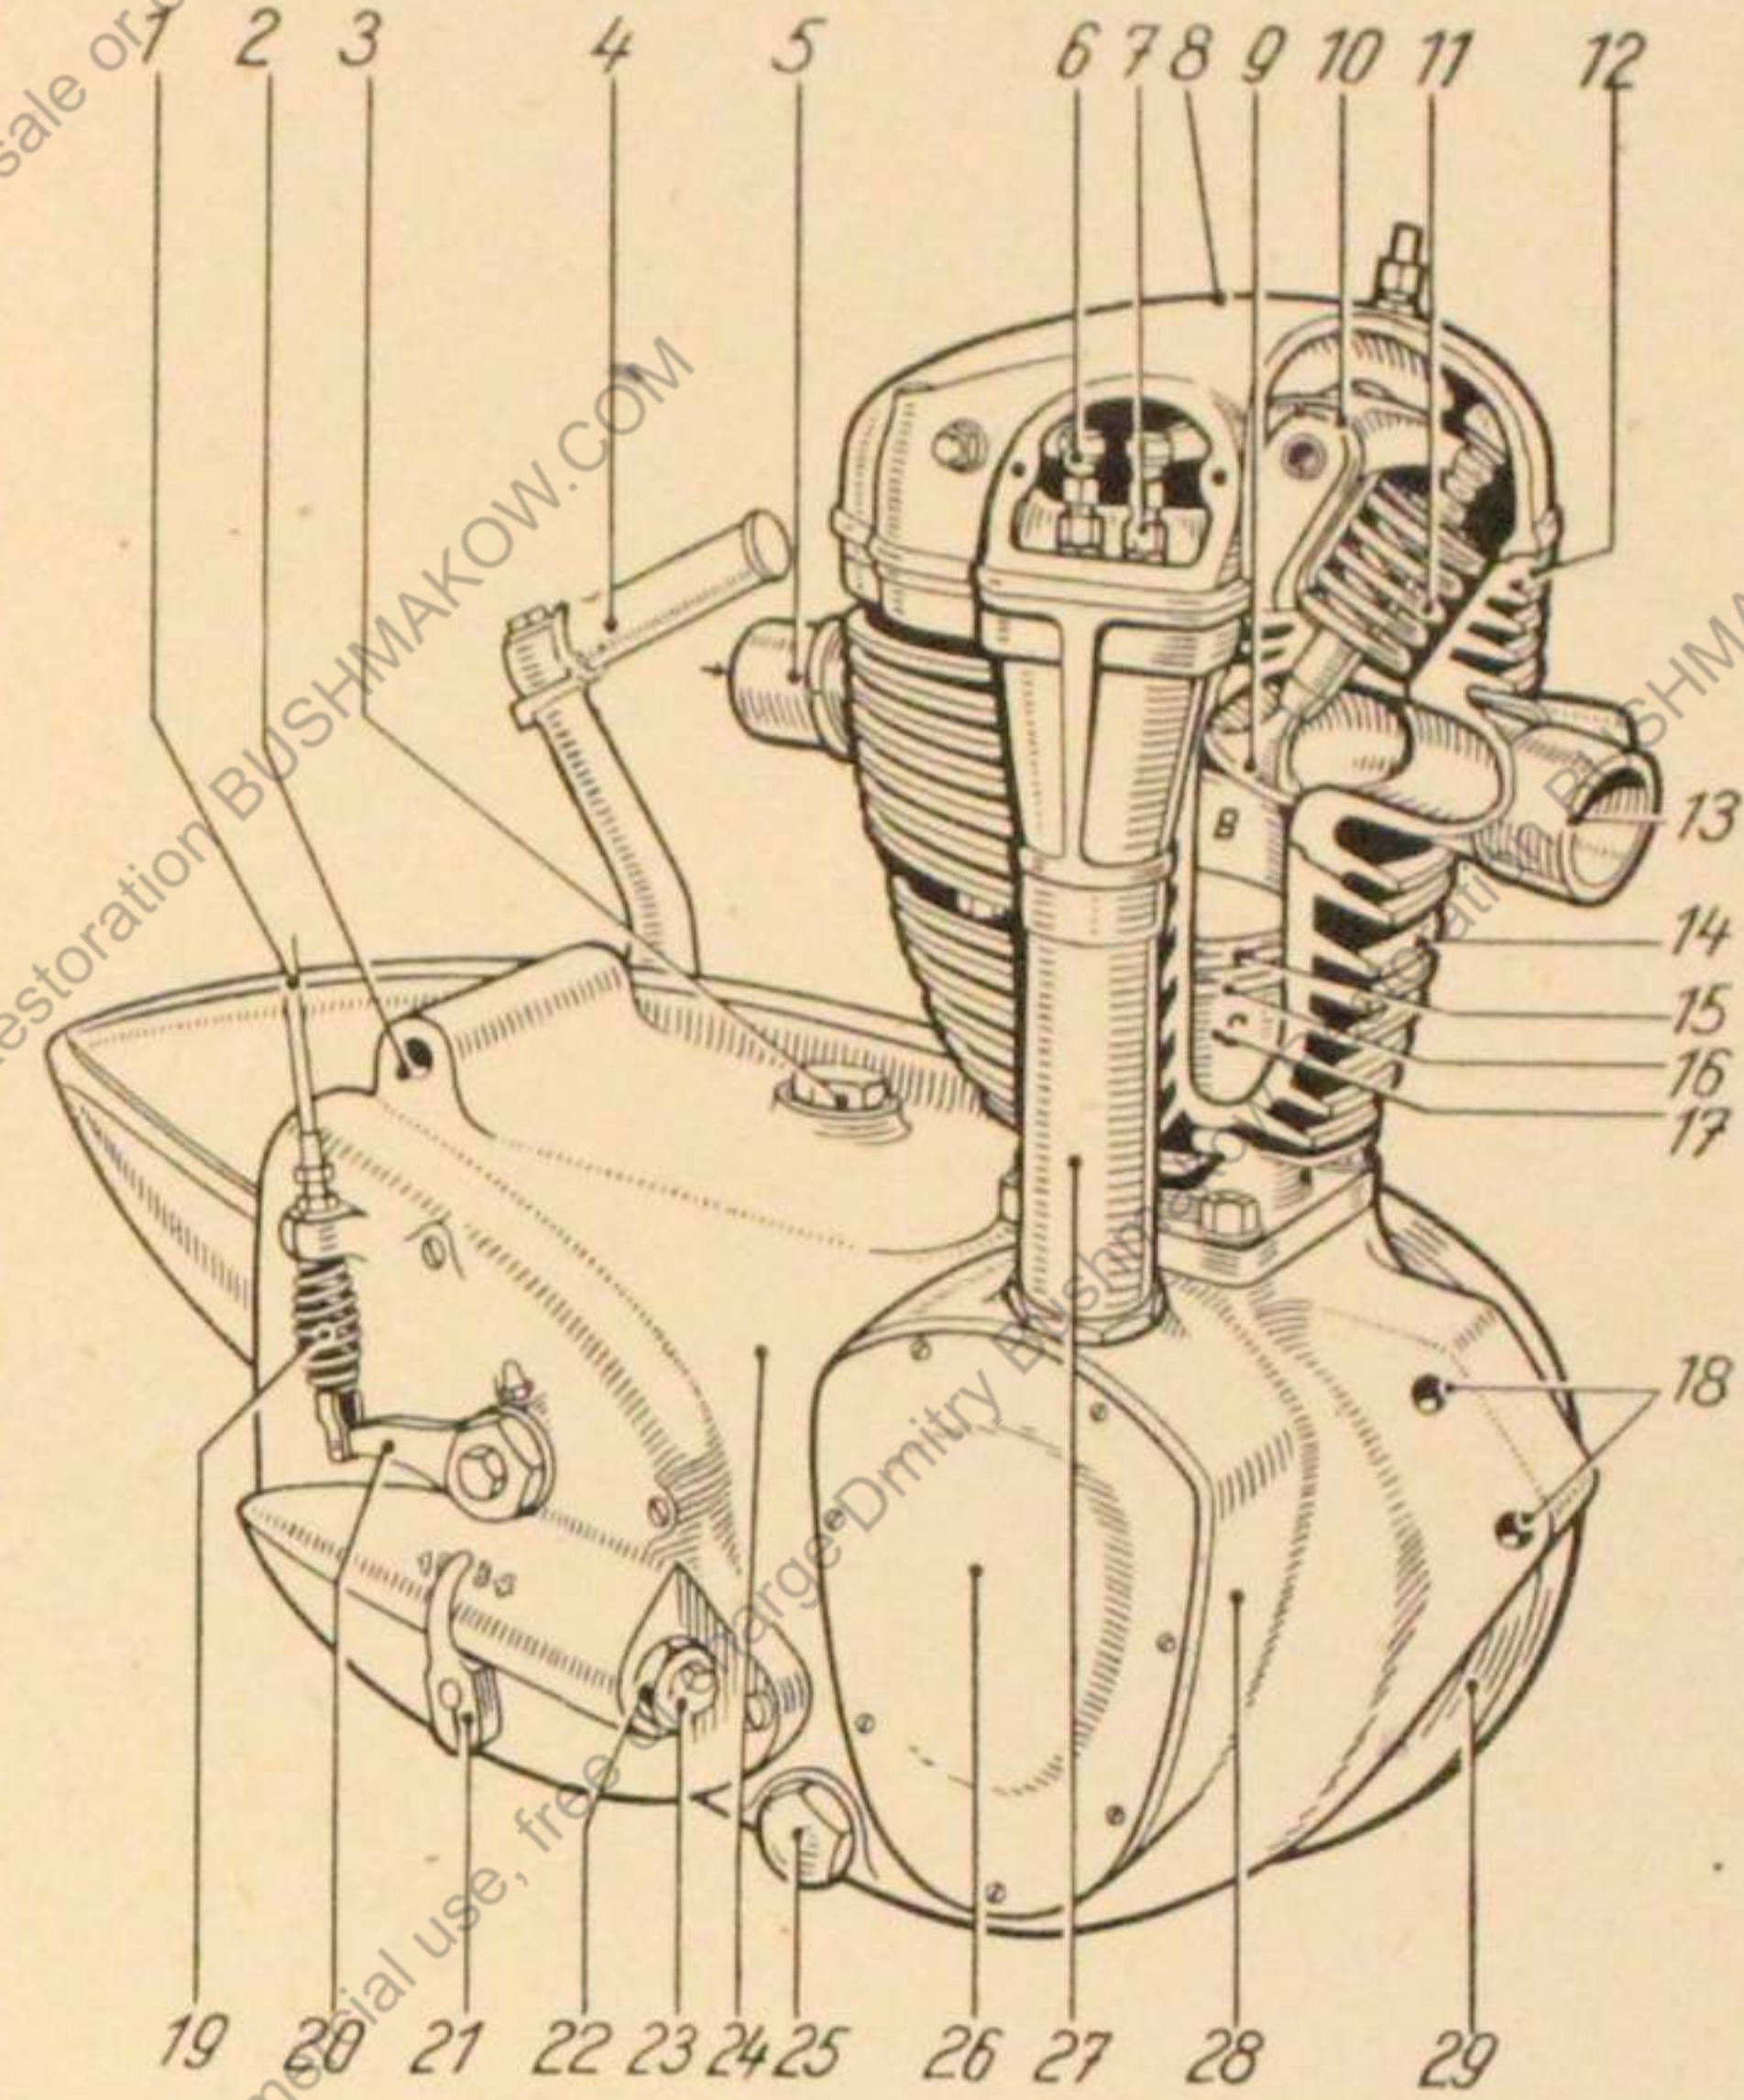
Motor, rechts, mit geöffneter Ventilkammer
